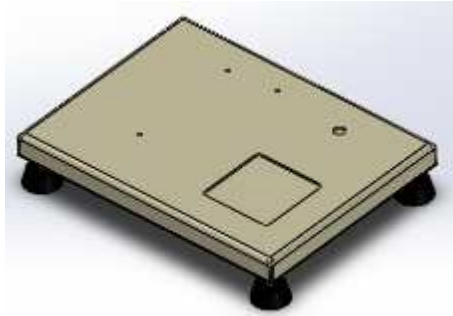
Estructura metálica o caja base. Fuente: Autor.
